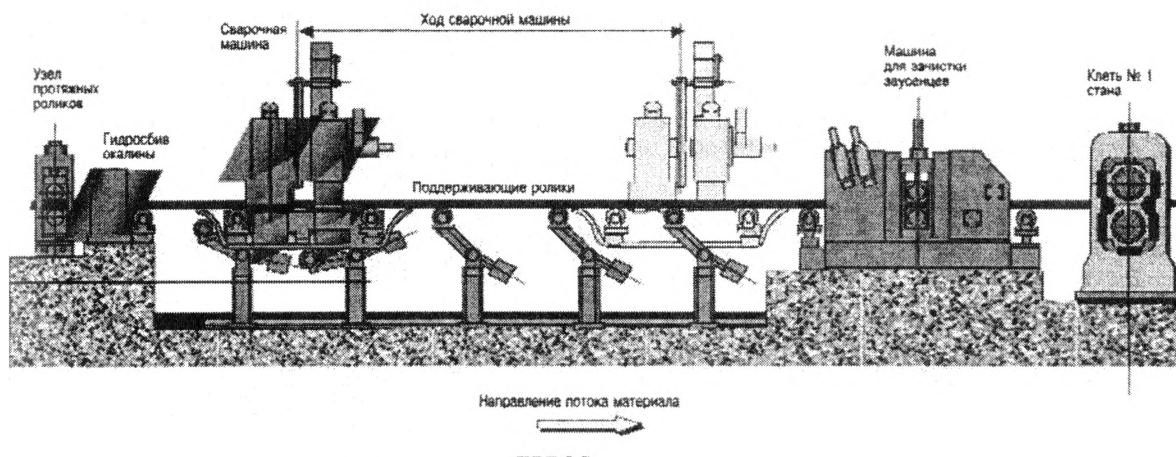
Схема установки стыковой сварки системы EBROS
